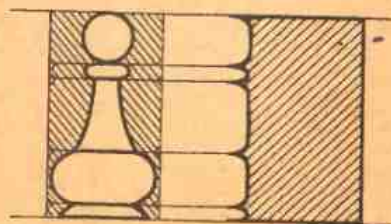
Шаблон для нанесения рисунка токарного изделия
